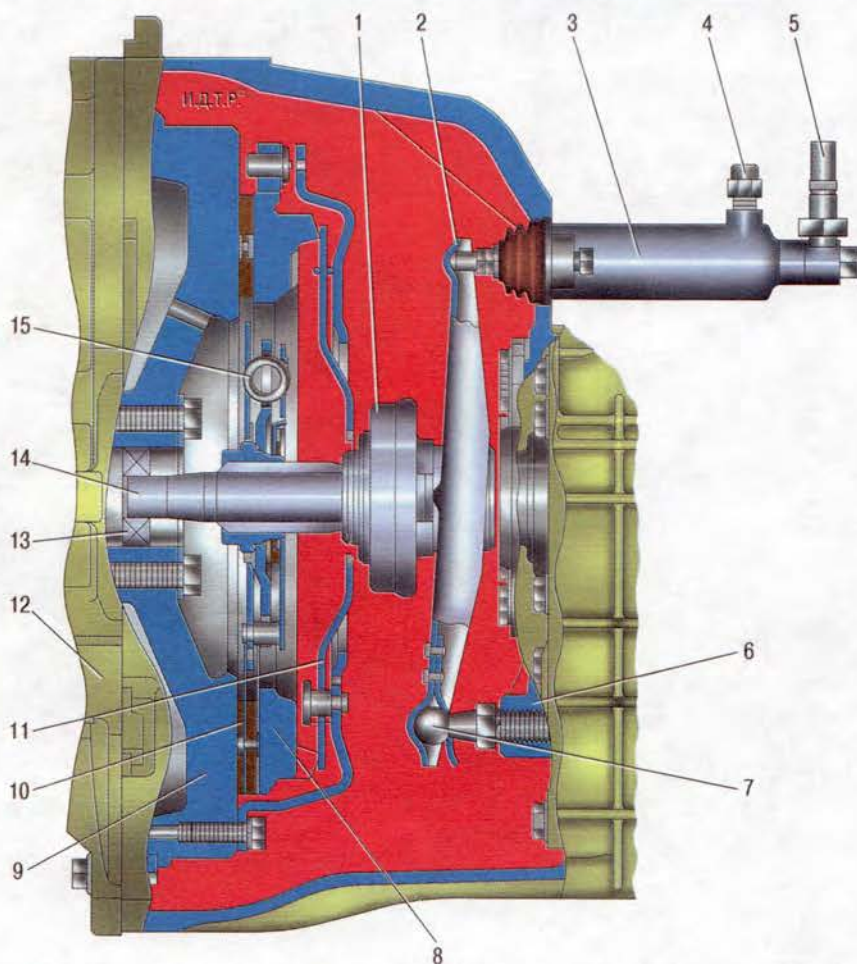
Сцепление: 1 – подшипник выключения сцепления; 2 – вилка подшипника выключения сцепления; 3 – рабочий цилиндр выключения сцепления; 4 – клапан для удаления воздуха; 5 – шланг; 6 – картер сцепления; 7 – опора вилки; 8 – нажимной диск; 9 – маховик коленчатого вала; 10 – ведомый диск; 11 – диафрагменная пружина; 12 – усилитель картера сцепления; 13 – передний подшипник первичного вала коробки передач; 14 – первичный вал; 15 – гаситель крутильных колебаний
